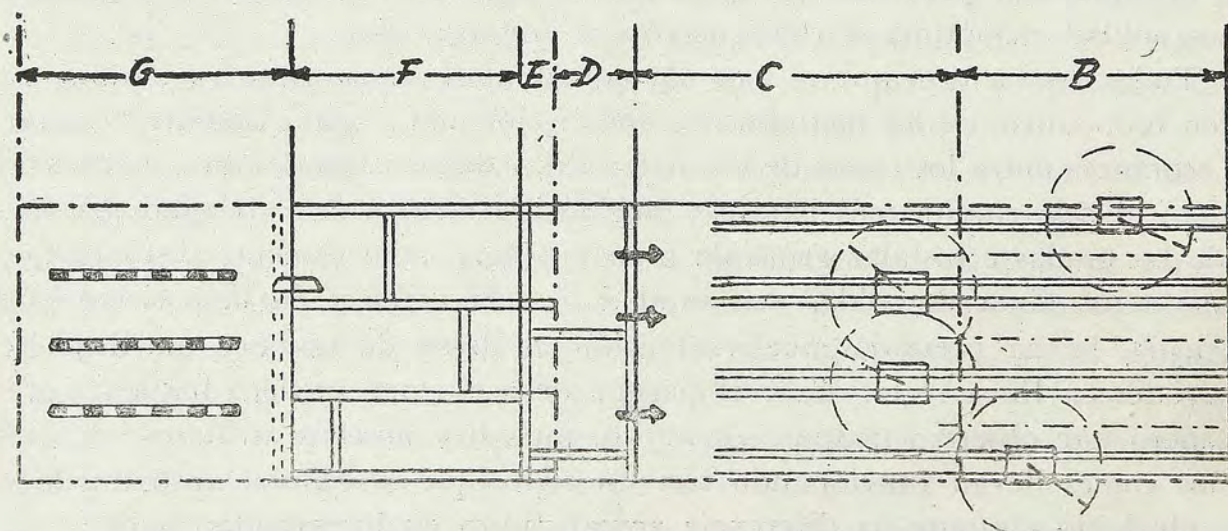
Esquema de disposición de astillero para soldadura, desarrollado en profundidad.
